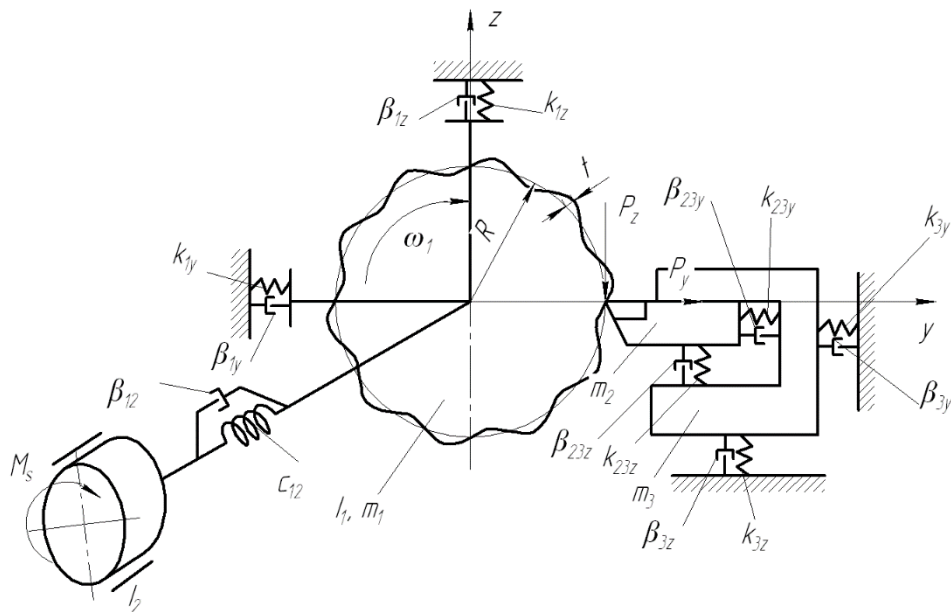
Розрахункова схема еквівалентної багатомасової системи для дослідження динаміки процесу токарної обробки поверхні із змінною глибиною різання
